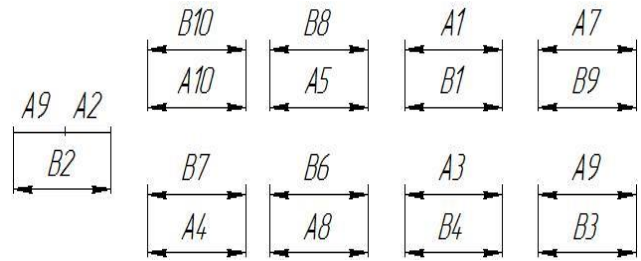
Схема розташування технологічних розмірних ланцюгів заготовки ролика
